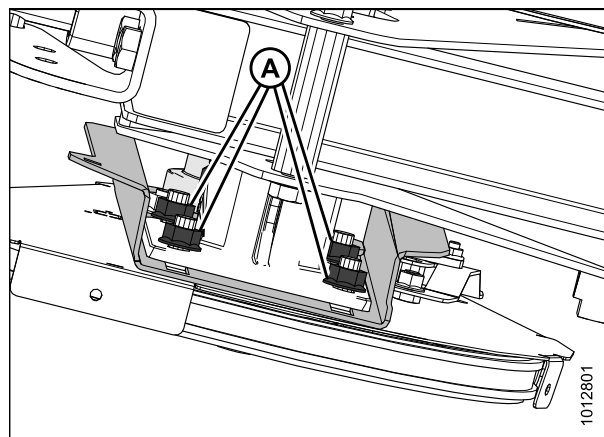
Привод единого мотовила — вид со стороны нижней части подбирающего мотовила
